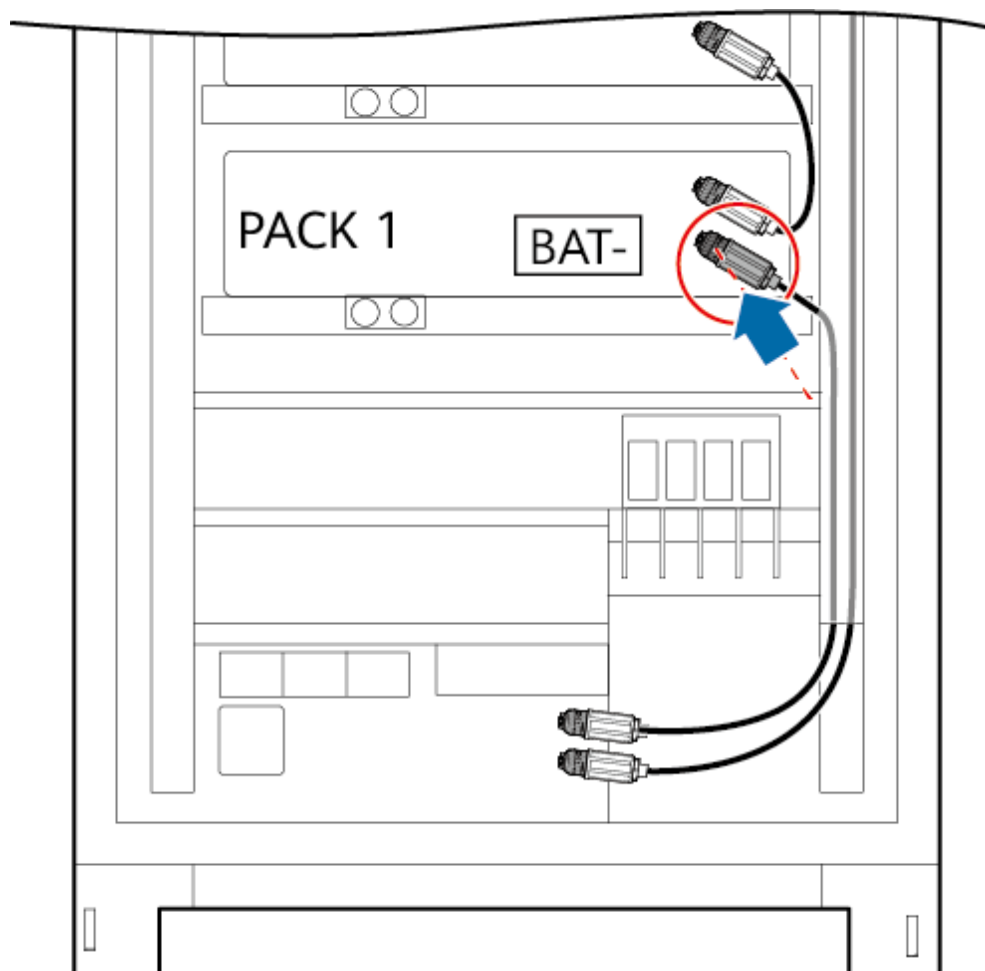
Collegamento di un terminale del cavo di alimentazione (modello 1)
